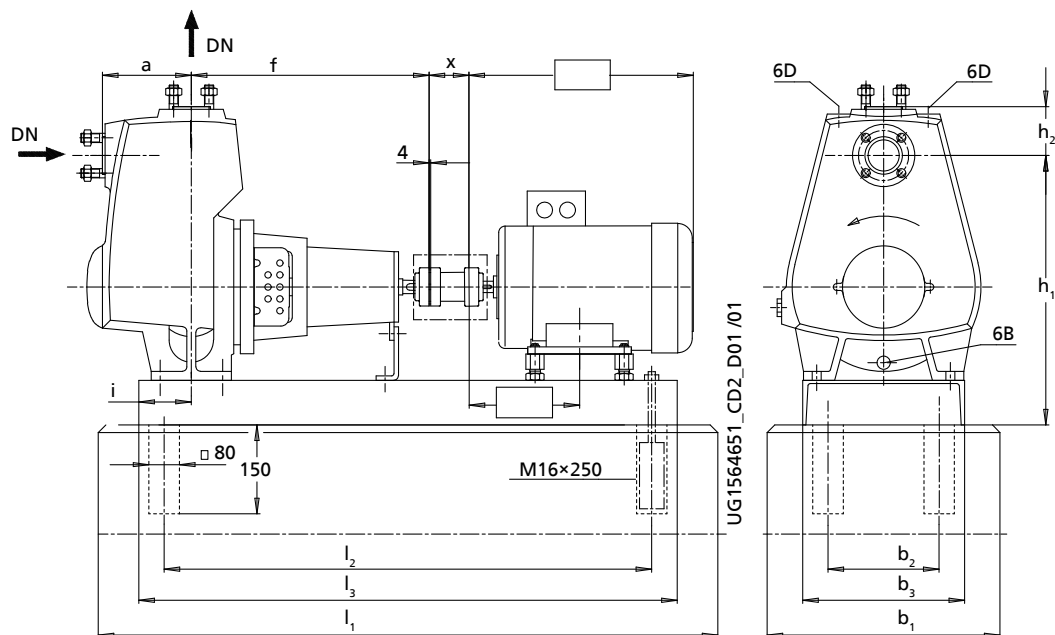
Габаритные размеры 040-040-140 до 125-125-260 (узел вала 25 / 35) - насосный агрегат с муфтой с промежуточной втулкой
